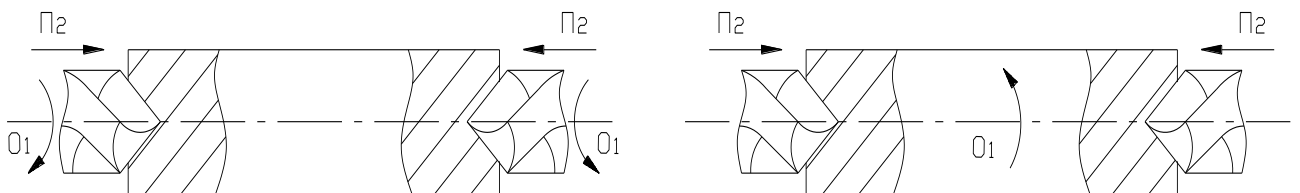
Схема обробки отворів циліндричними сверлами з рухомою (б) і нерухомою (а) заготовкою
